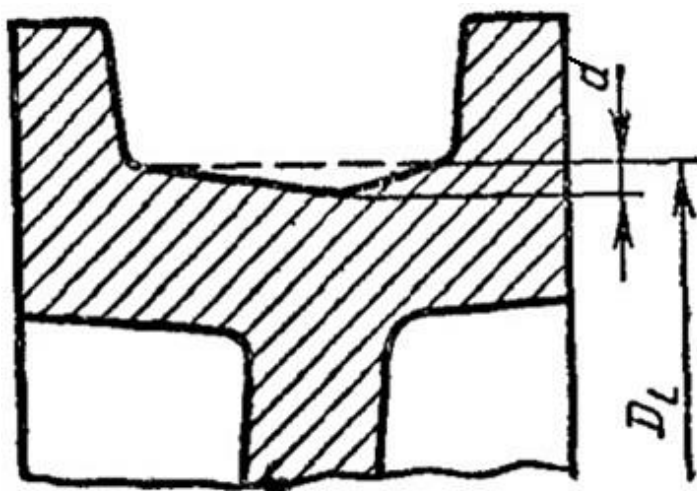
Зношування циліндричної поверхні ходового колеса
